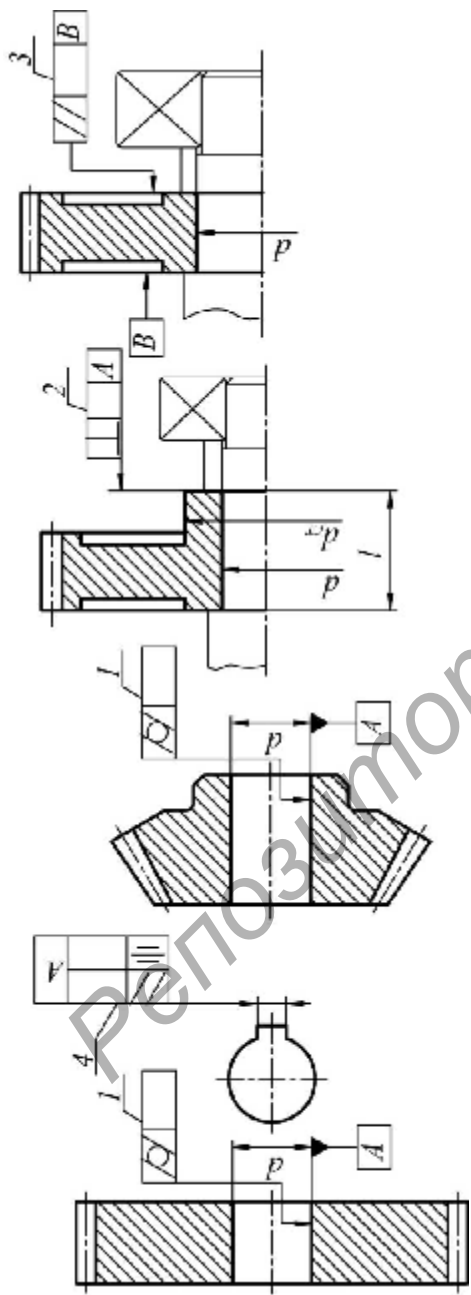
Допуски формы и расположения поверхностей
